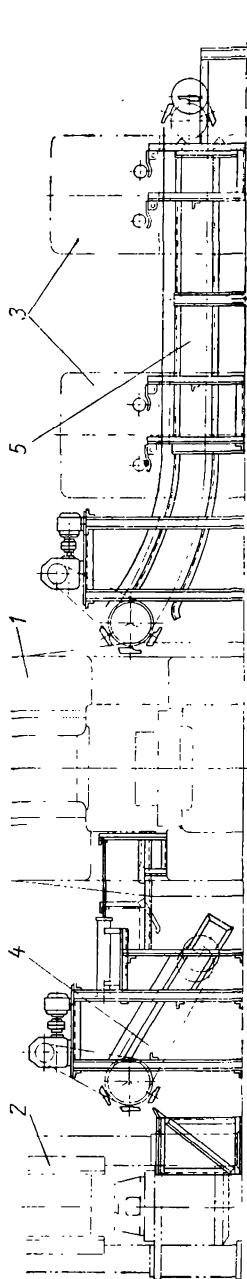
Принципиальная схема расположения наклонного и горизонтально-наклонного пластинчатых транспортеров в агрегате кривошипного горячештамповочного пресса: 1 — кривошипный горячештамповочный пресс; 2 — обрезной пресс; 3 — индукционные нагреватели; 4 — наклонный пластинчатый транспортер; 5 — горизонтально-наклонный пластинчатый транспортер
